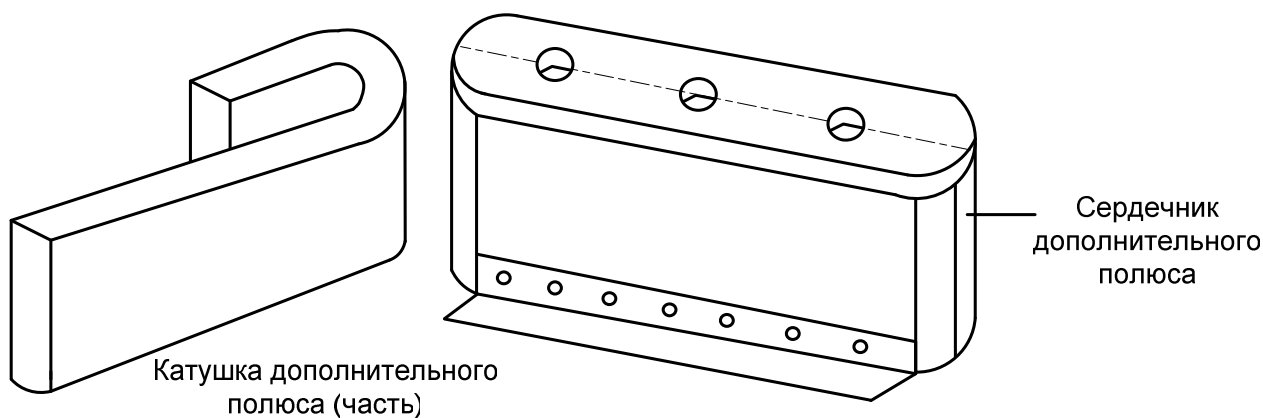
Дополнительный полюс тягового двигателя
